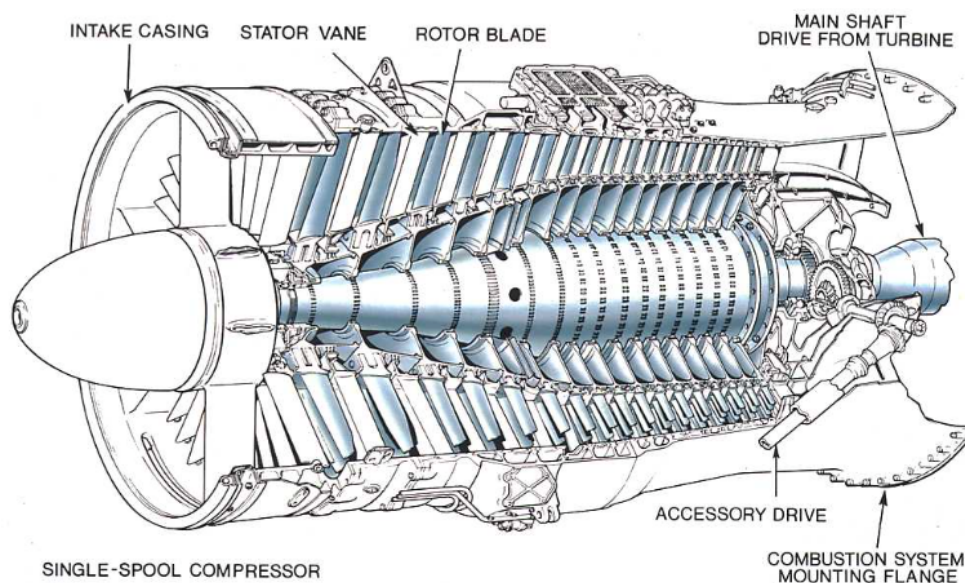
Vista cortada de um compressor *single-shaft turbojet* [3].
